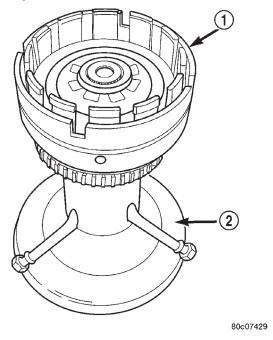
Conjunto de embrague de impulsión montado en la herramienta 8260
